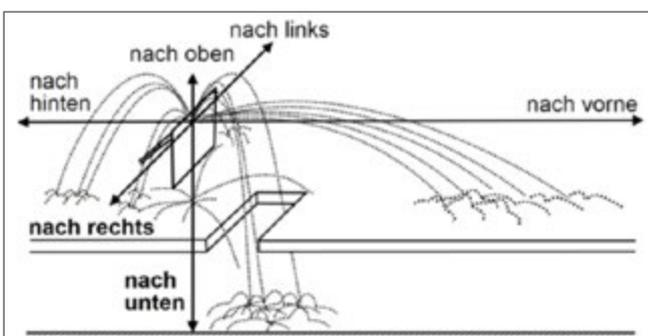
Funkenflug bei Schweißarbeiten
